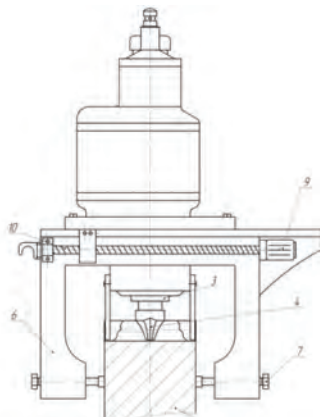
Главный вид приставного вертикального зубофрезерного станка
